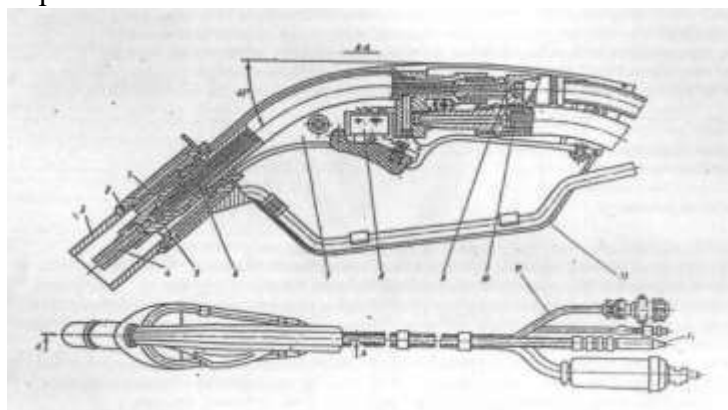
Сварочная горелка ГДПГ-301-8
